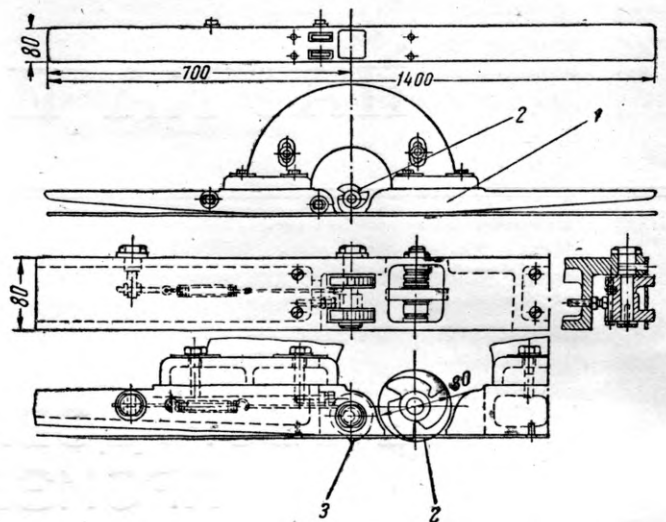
Устройство гибкой направляющей линейки к станку ЛЫФ
